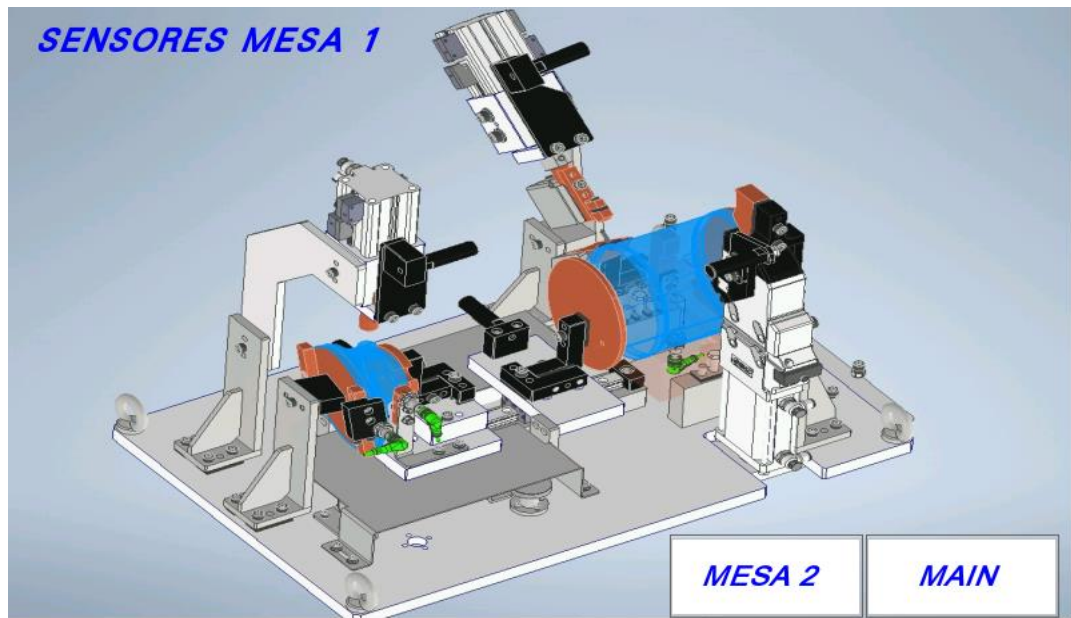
Layout mesa 1 sin indicadores de sensores. Fuente. elaboración propia
